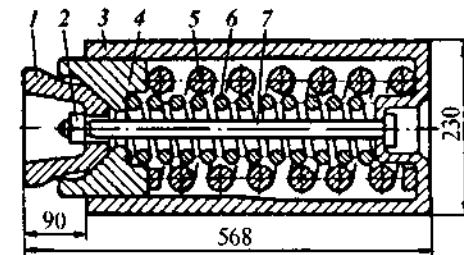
Пружинно-фрикционный поглощающий аппарат автосцепки грузовых вагонов. 1 — штампованный нажимной конус; 2 и 7 — стяжной болт и гайка; 3 — литой корпус; 4 — штампованный фрикционный клин; 5 и 6 — наружная и внутренняя пружины
